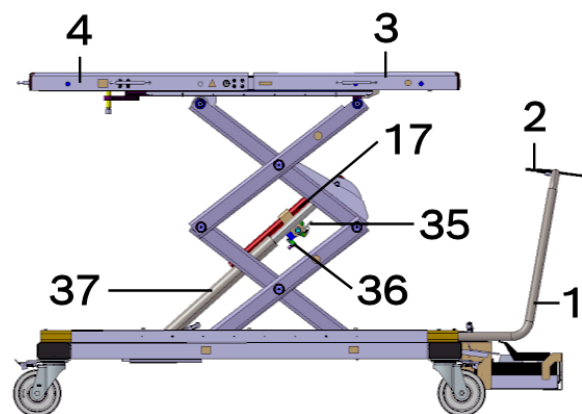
Mesa elevadora de tijeras sin fuelle protector
